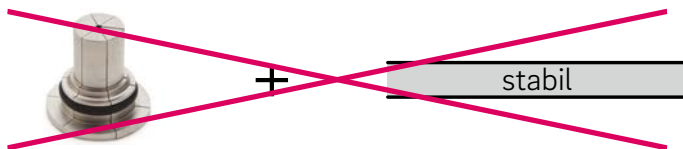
Unzulässige Aufweitwerkzeuge
